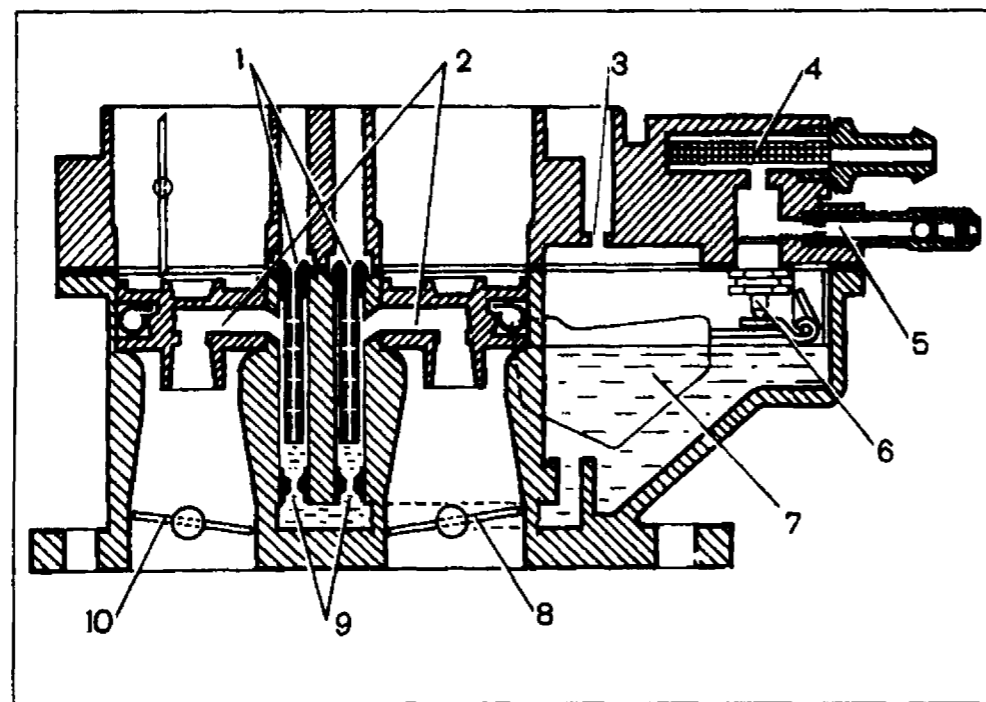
Схема главных дозирующих систем: 1 — главные воздушные жиклеры с эмульсионными трубками; 2 — распылители первой и второй камер; 3 — балансировочное отверстие; 4 — топливный фильтр; 5 — патрубок с калиброванным отверстием слива части топлива в топливный бак; 6 — игольчатый клапан; 7 — поплавок; 8 — дроссельная заслонка второй камеры; 9 — главные топливные жиклеры; 10 — дроссельная заслонка первой камеры
